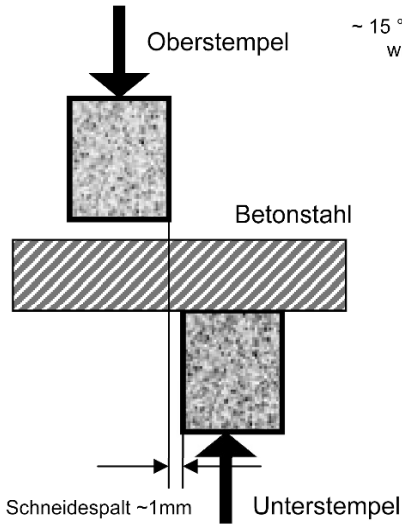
Schneideschema von Betonstahl in seitlicher Sicht
